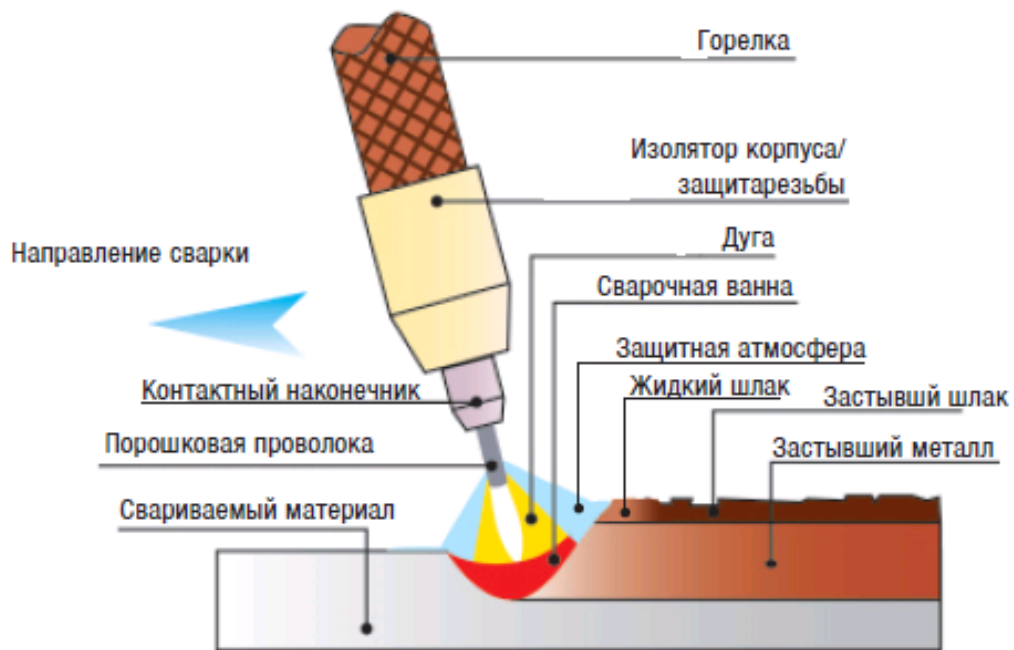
Схема выполнения сварки порошковой проволокой
